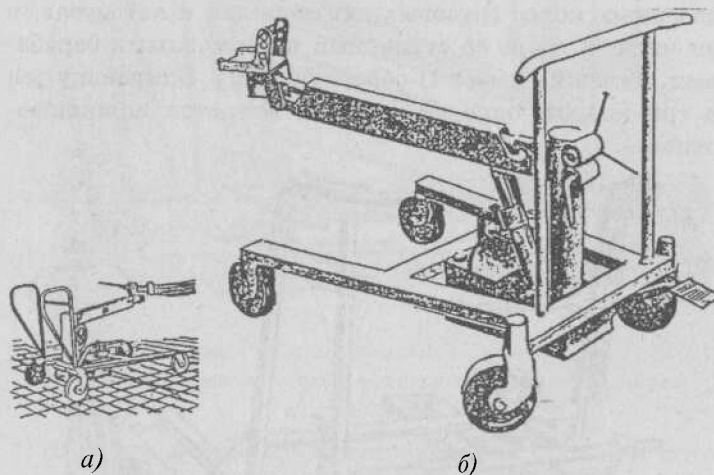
Общий вид тележки П-216 для снятия-установки рессор грузовых автомобилей
